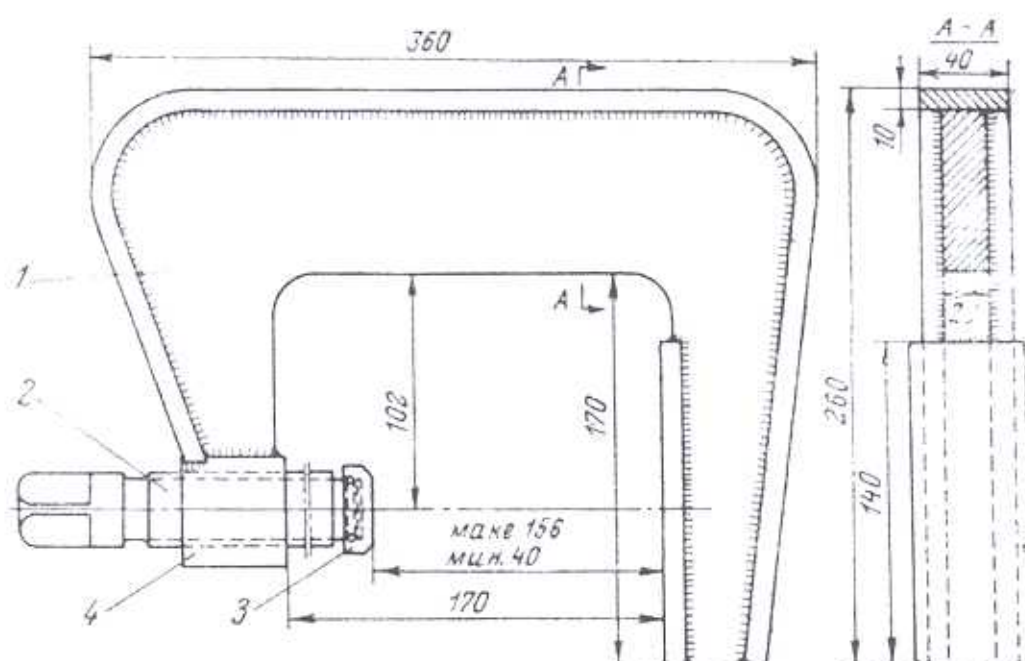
Струбцина для зажима меди обмотки ротора при рихтовке:
